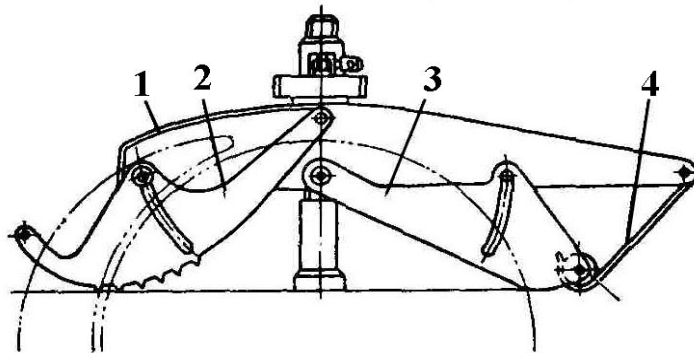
Будова пили кругло пильного верстата для поздовжнього розпилування, що огорожує:
